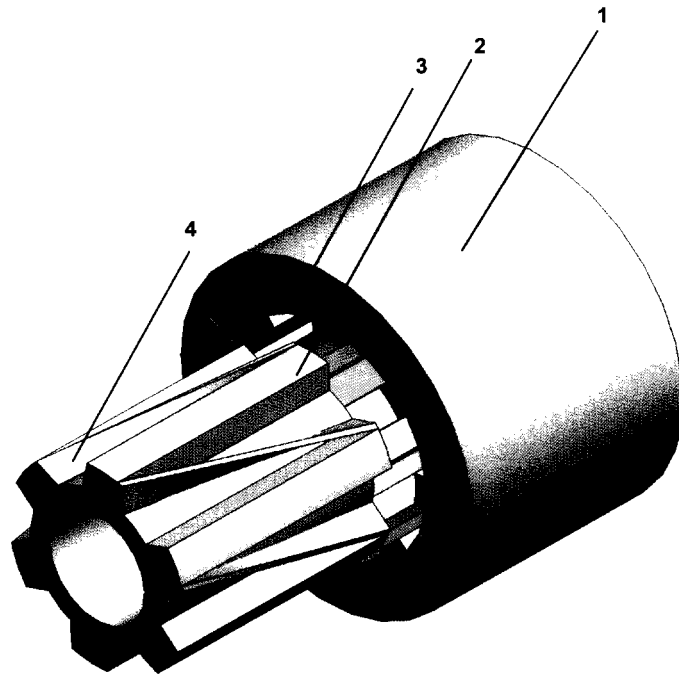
Vederea în spațiu a motorului cu rotorul extras spre exterior
